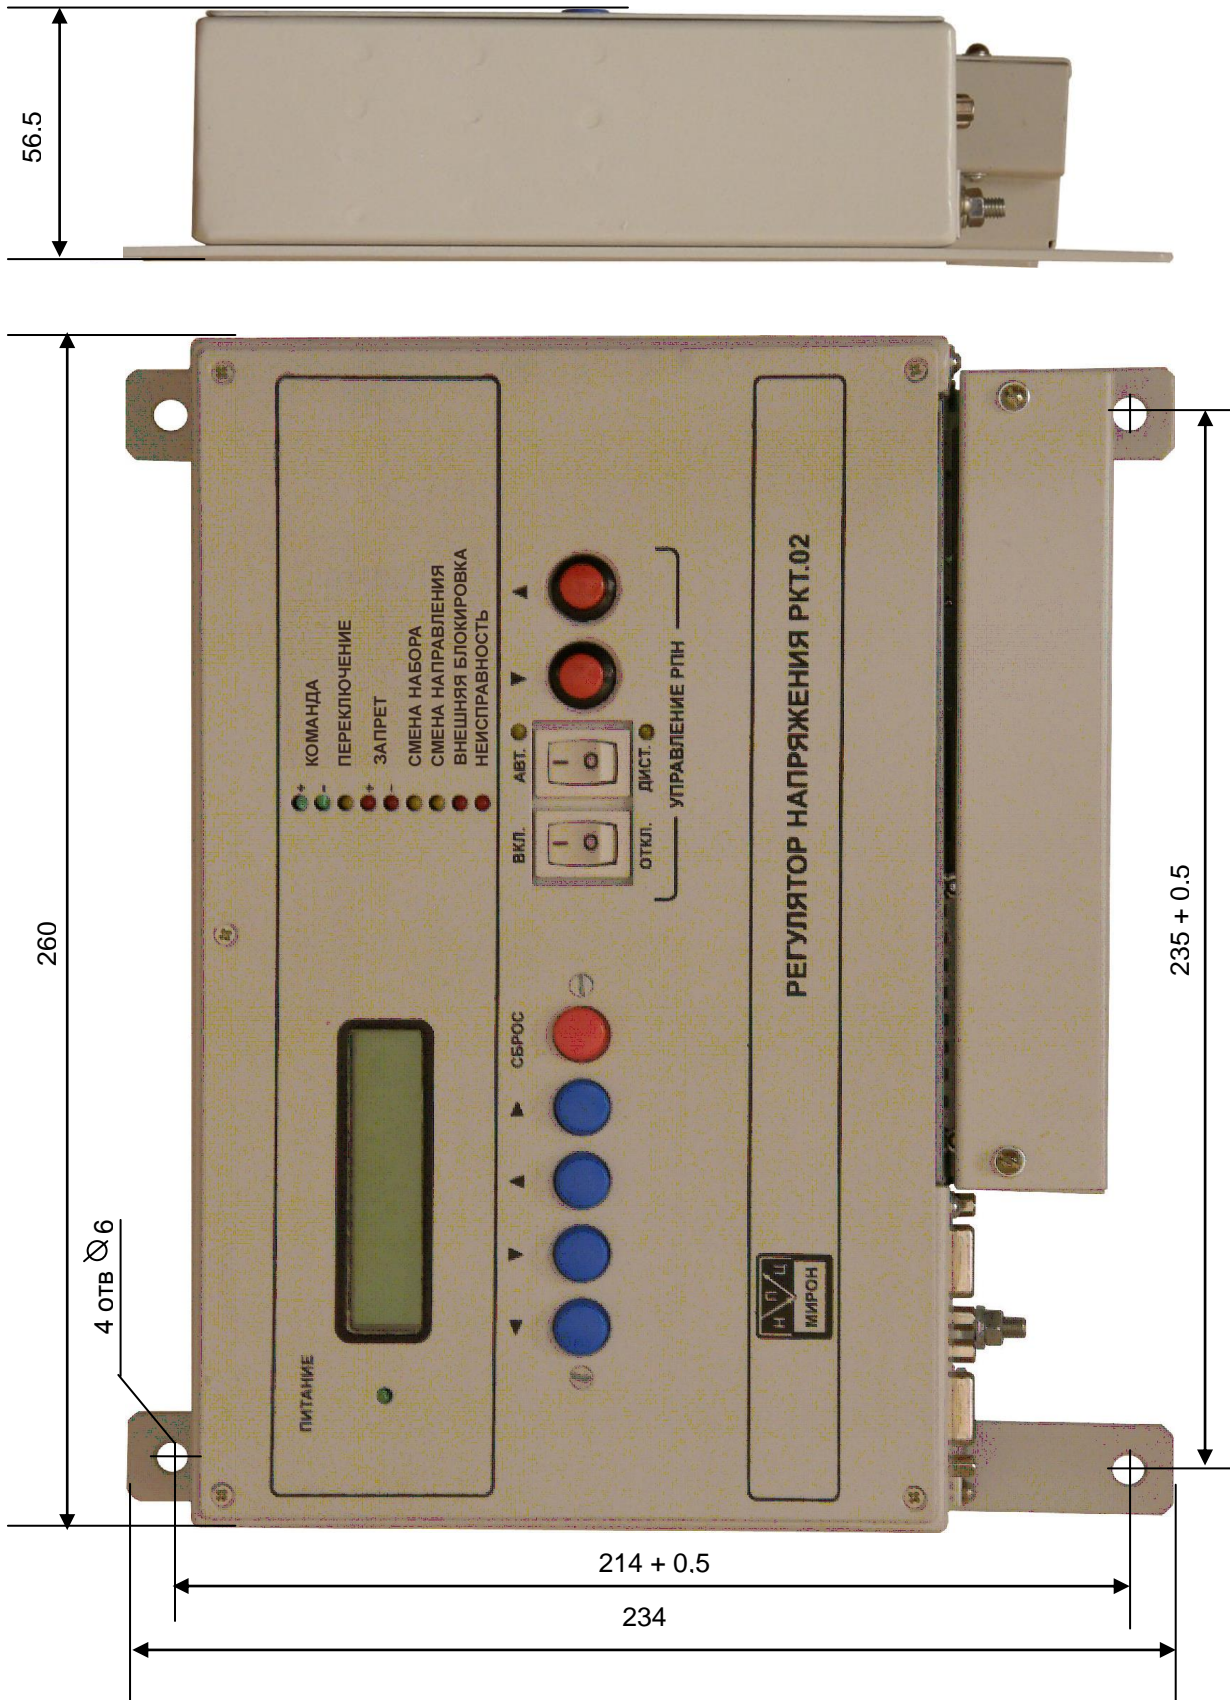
Габаритный чертёж базового исполнения прибора
